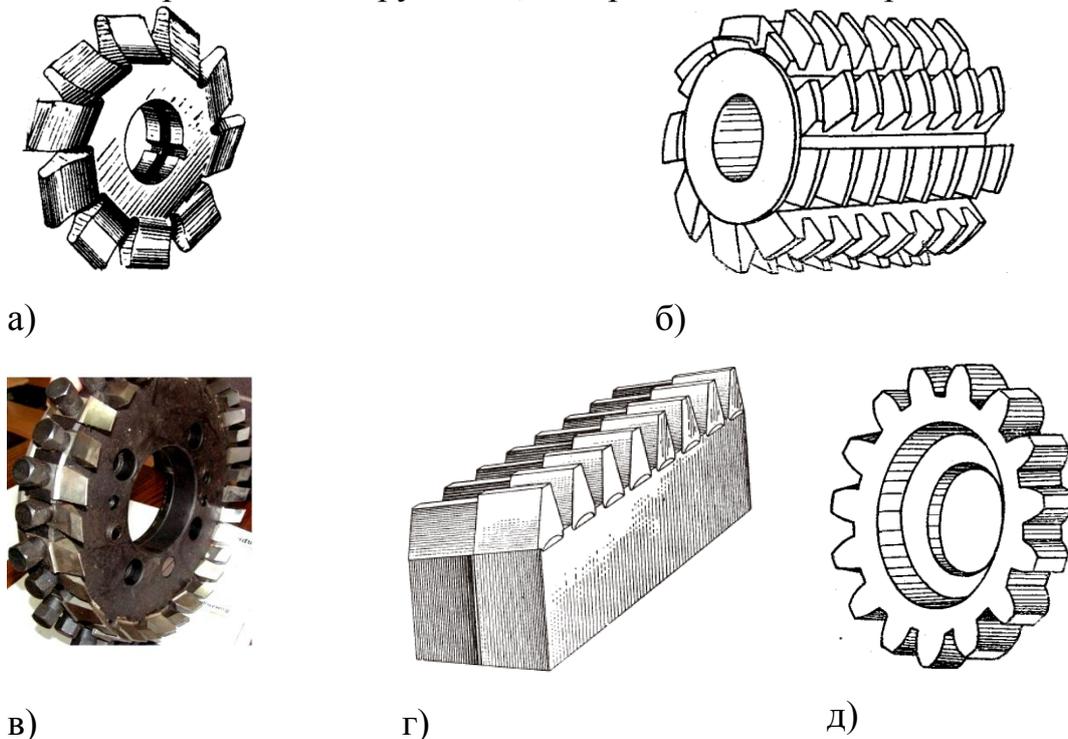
Виды зуборезных инструментов: а) дисковая фреза; б) червячная фреза; в) зуборезная головка; г) рейка; д) долбяк
